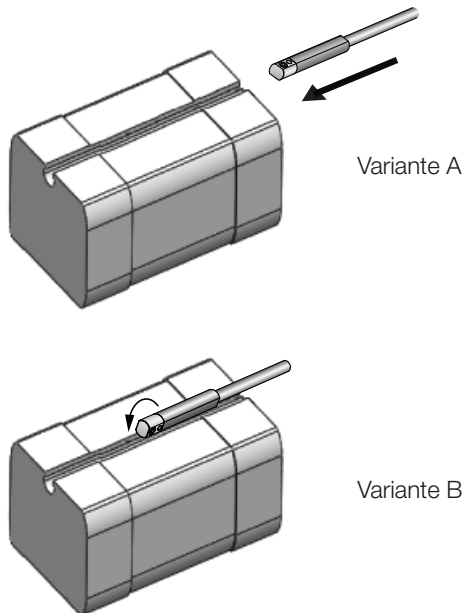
Montaje BMF 203K-... en dos variantes
